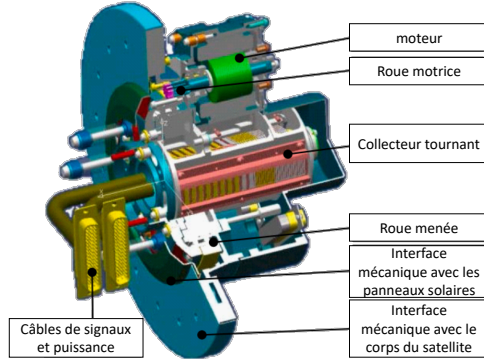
Composition du Solar Array Drive Assembly (SADA)
